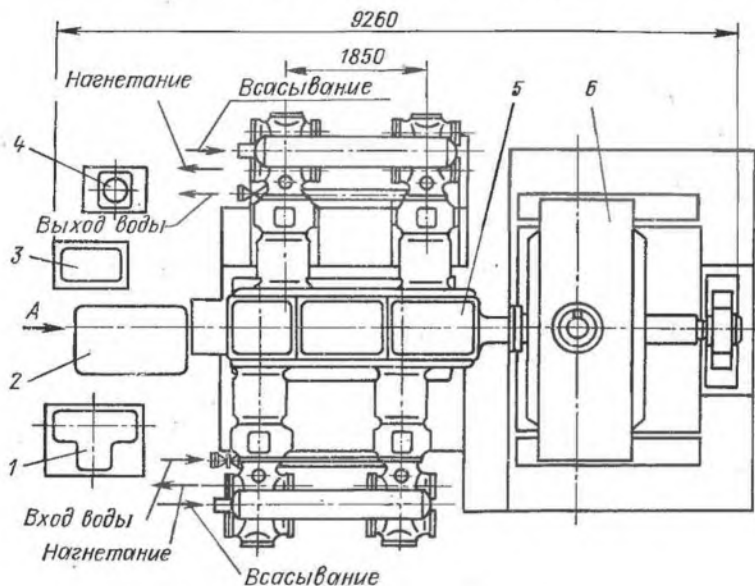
Компрессорная установка с компрессором 4ГМ16-45/35-55СМ2
